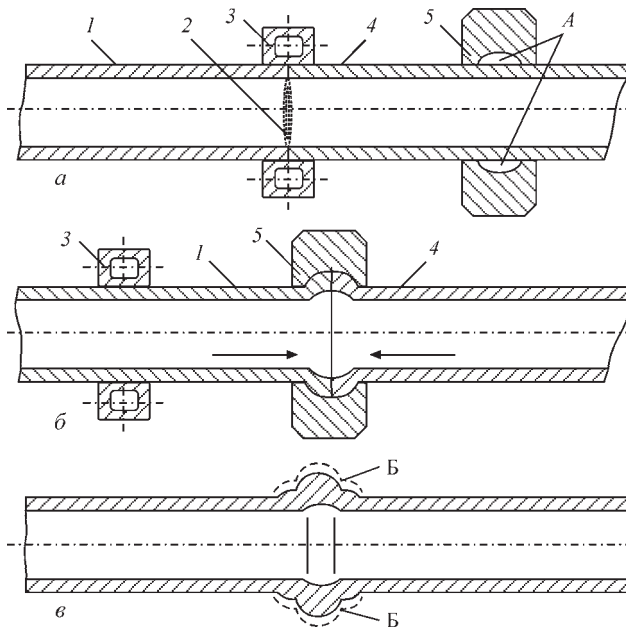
Схема формування зварного шва у процесі індукційного зварювання тиском з використанням спеціального пристрою, формуючого зовнішній валик заданої форми [19, 21]: процес нагрівання (а); процес осадження (б); отримане зварне з'єднання (в); 1 і 4 – зварювальні трубні деталі; 2 – активуючі речовини у зварному шві; 3 – кільцевий індуктор; 5 – формуючий пристрій; А – формуюча внутрішня поверхня пристрою; Б – отримана зовнішня поверхня зварного шва
